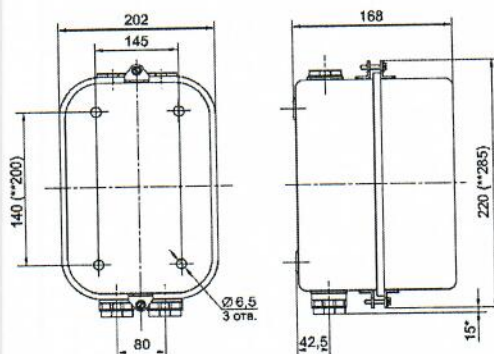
Пускатель ПМ12-063 63А в защитном корпусе. Степень защиты - IP40; IP54
